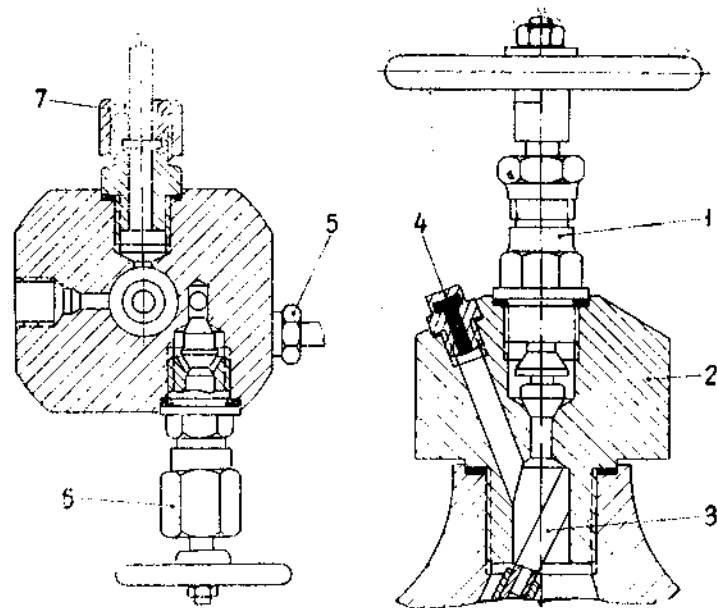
Головка дополнительного баллона: 1—перепускной вентиль; 2—корпус головки; 3—дренажная трубка; 4—штуцер с плавким металлом; 5—штуцер; 6—продувочный вентиль; 7—гайка штуцера
